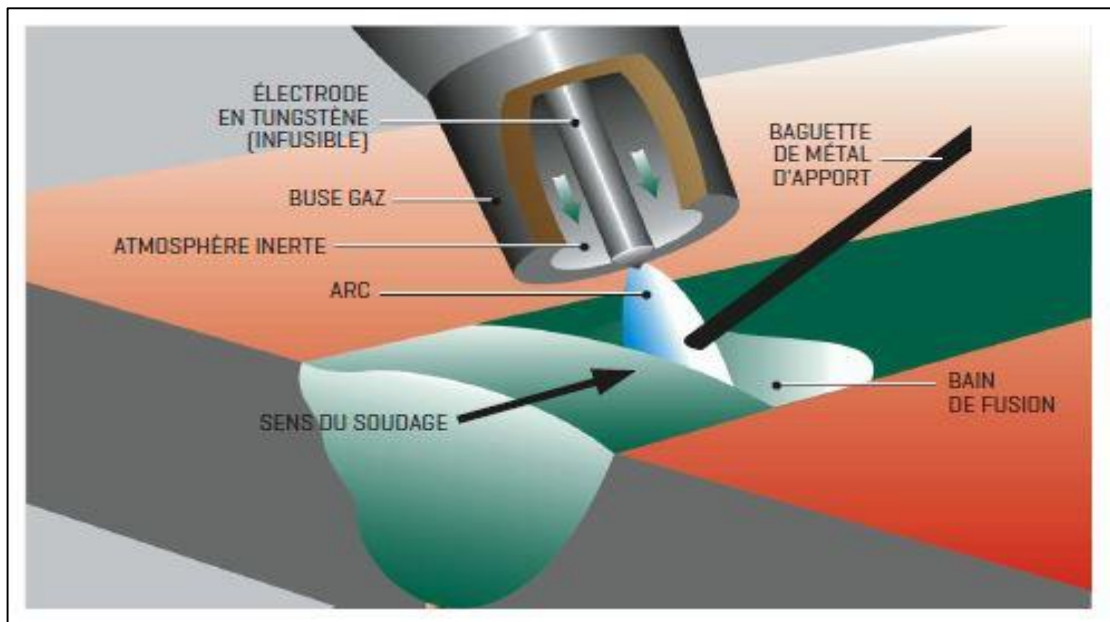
Soudage TIG (Tungstène Inerte Gaz) [19]
